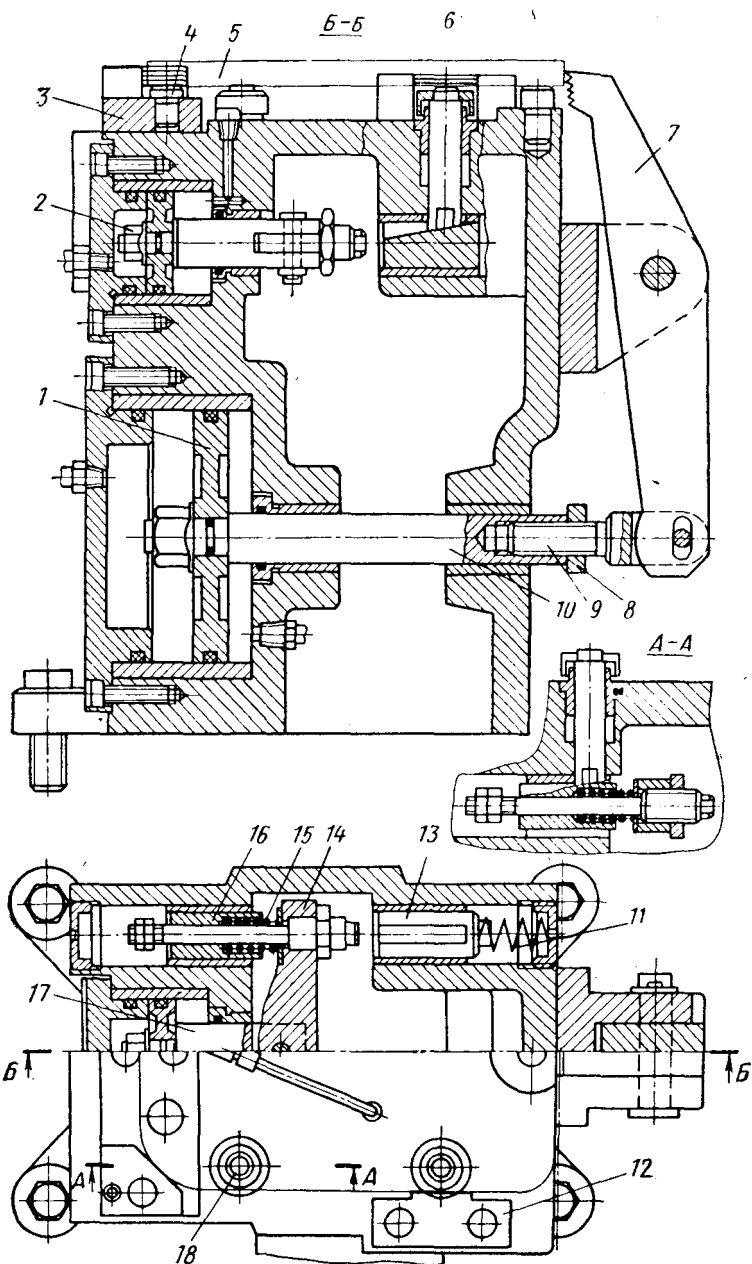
Приспособление для фрезерования крышек с механизацией подвода и стопорения дополнительных опор
